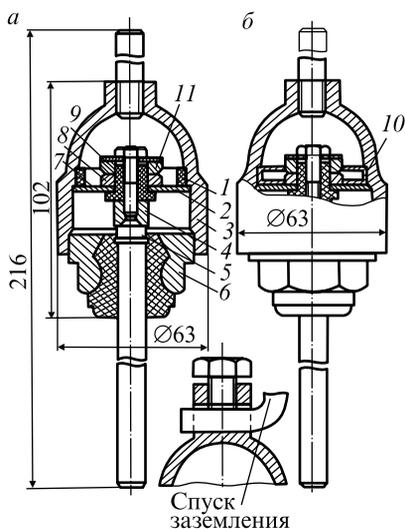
Искровые промежутки ИПМ с пластмассовыми (а) и металлическими (б) экранами; 1 — кольцевой пластмассовый экран; 2 — стальная шайба; 3 — крышка; 4 — гайка; 5 — изолированный стержень; 6 — корпус; 7 — втулка изолирующая; 8, 9 — шайба контактная; 10 — металлический экран; 11 — слюдяная прокладка
